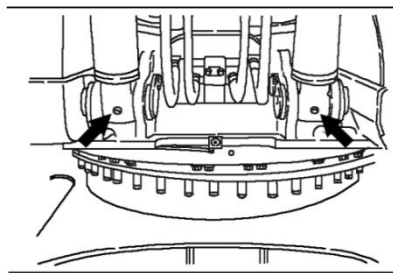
1. Расположение пресс-маленок в цилиндрах стрел
